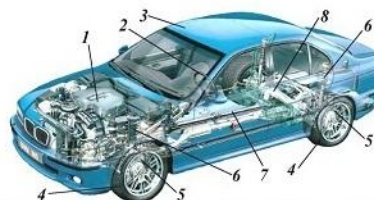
Устройство легкового автомобиля: 1 - двигатель; 2 - рулевое управление; 3 - кузов; 4 - движители колесного типа; 5 - тормозное управление; 6 - подвеска; 7 - трансмиссия; 8 - усиленный каркас кузова.
